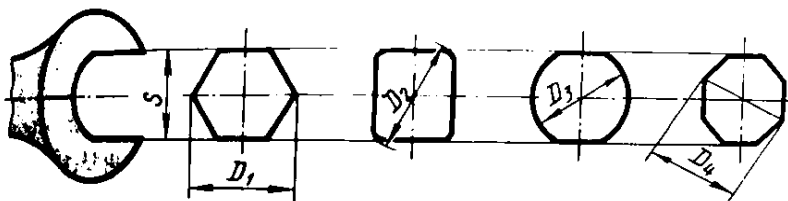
Размеры под ключ и определение диаметра заготовки
